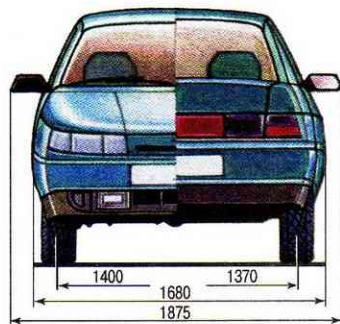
Габаритные размеры автомобиля ВАЗ-2111
